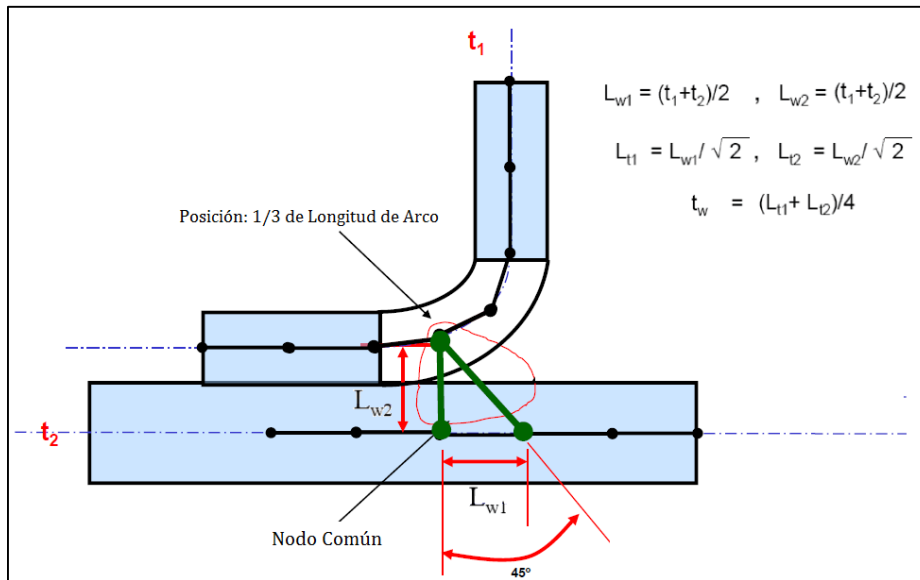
Modelado FEM Unión Soldada en "L" [29]
